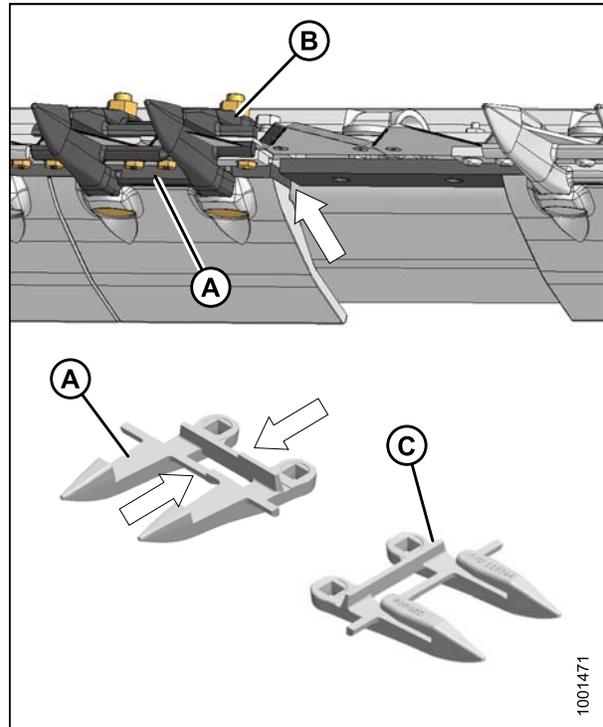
Противорежущий палец на жатке с двумя ножами
